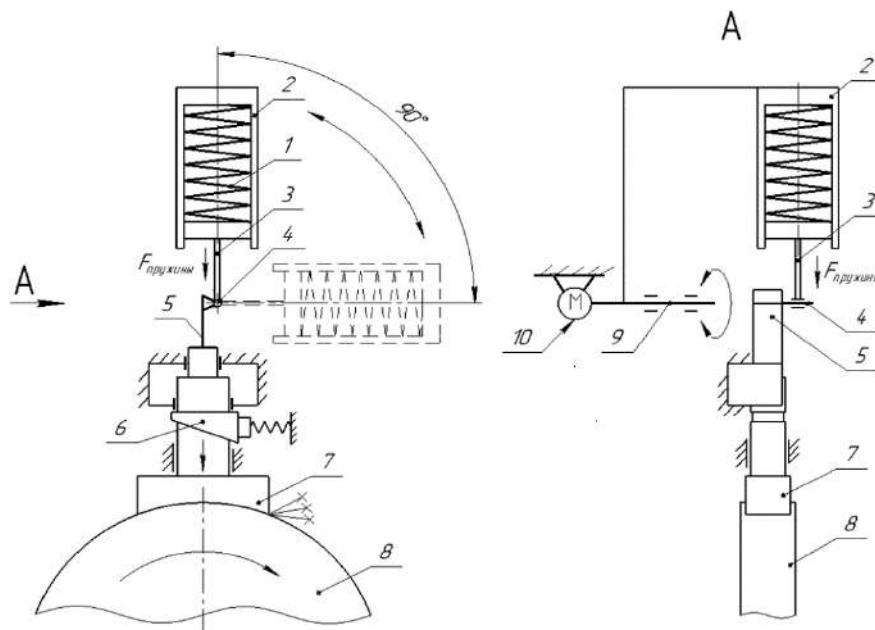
Схема предлагаемого тормозного механизма МТС
